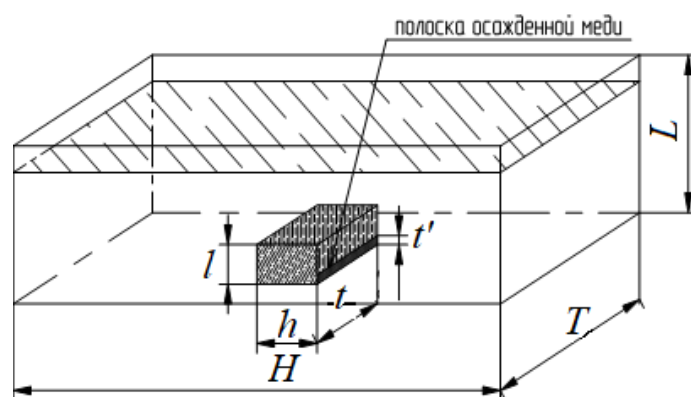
Промежуточный этап изготовления контрольного образца из неметалла с использованием подготовительного бруска с нанесенной полоской меди
